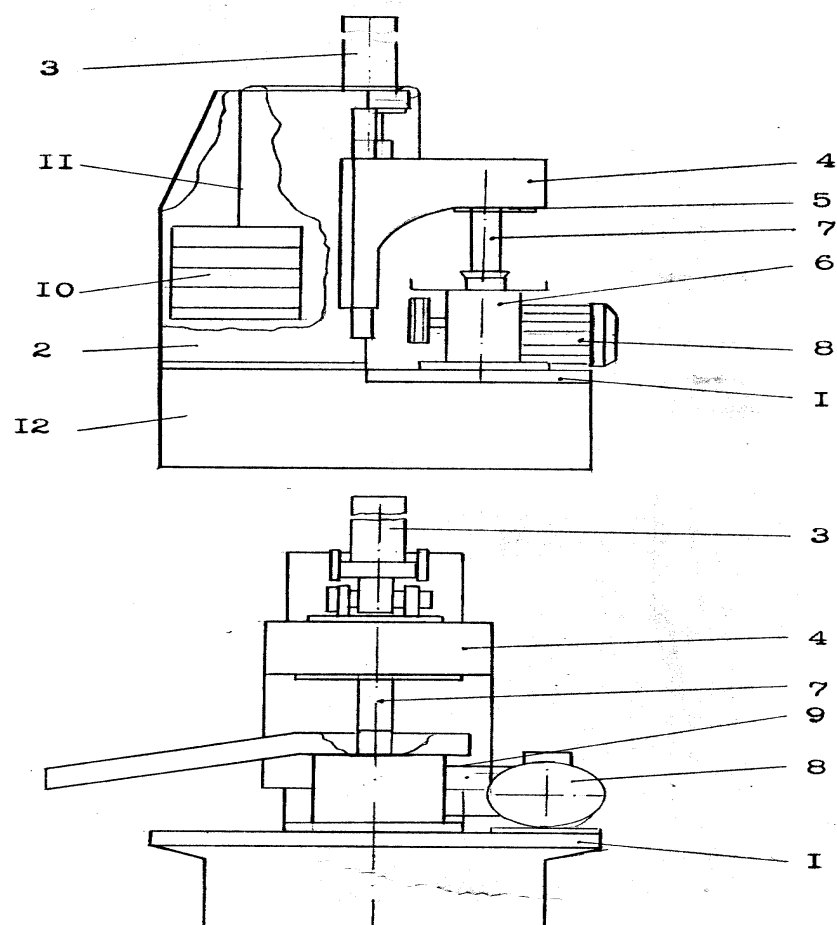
Схема экспериментального стенда: 1- рабочий стол: 2- станина 3- гидроцилиндр: 5- опорное устройство: 6- ударный механизм: 7- блок отливков: 8- электродвигатель: 9- ременная передача: 10- противовес: 11- трос: 12- основание.
